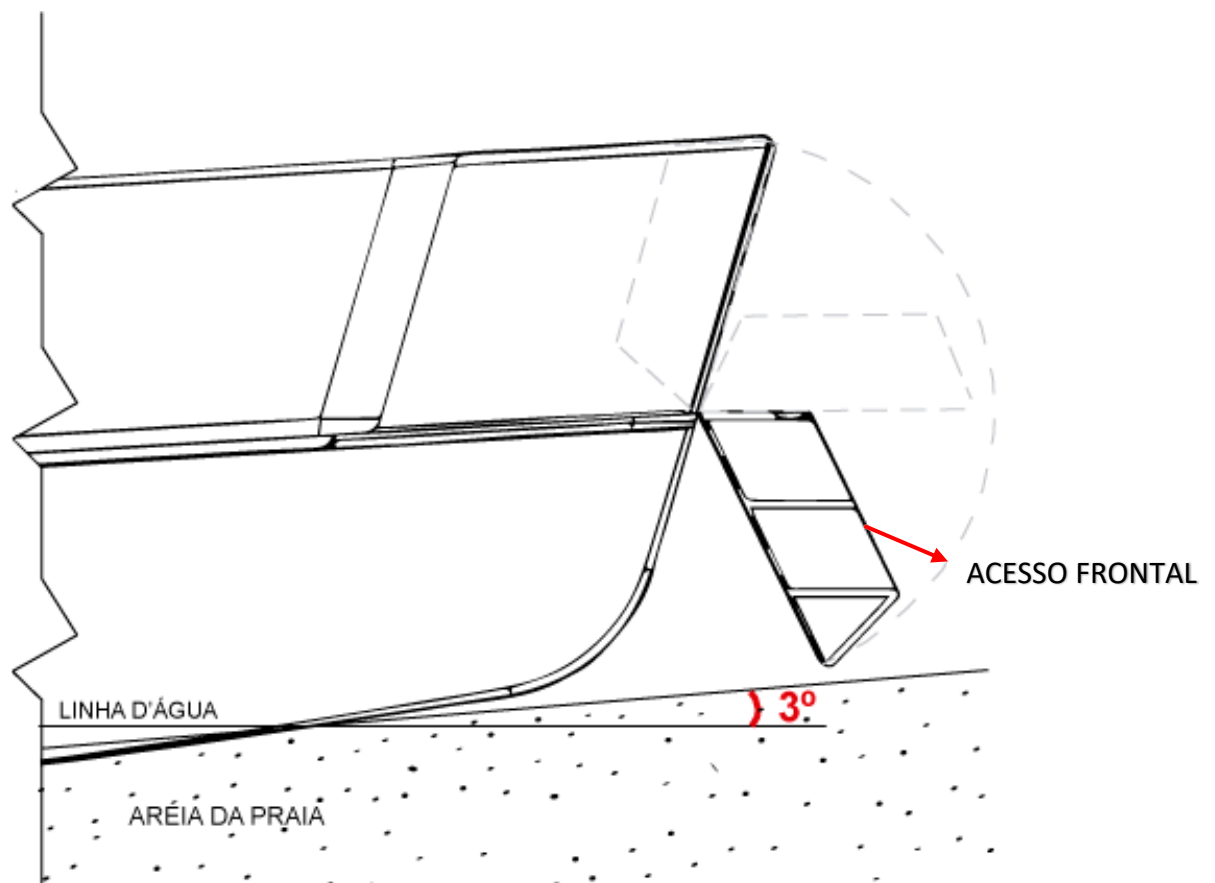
Síntese de Solução de Design Acesso Frontal - Escada
